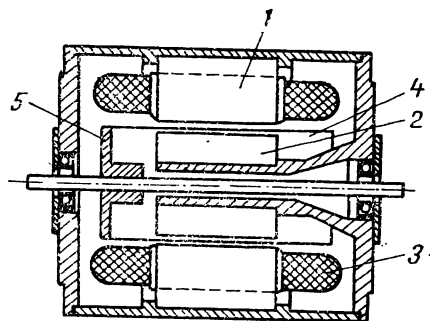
Servomotor cu rotor în formă de pahar:
